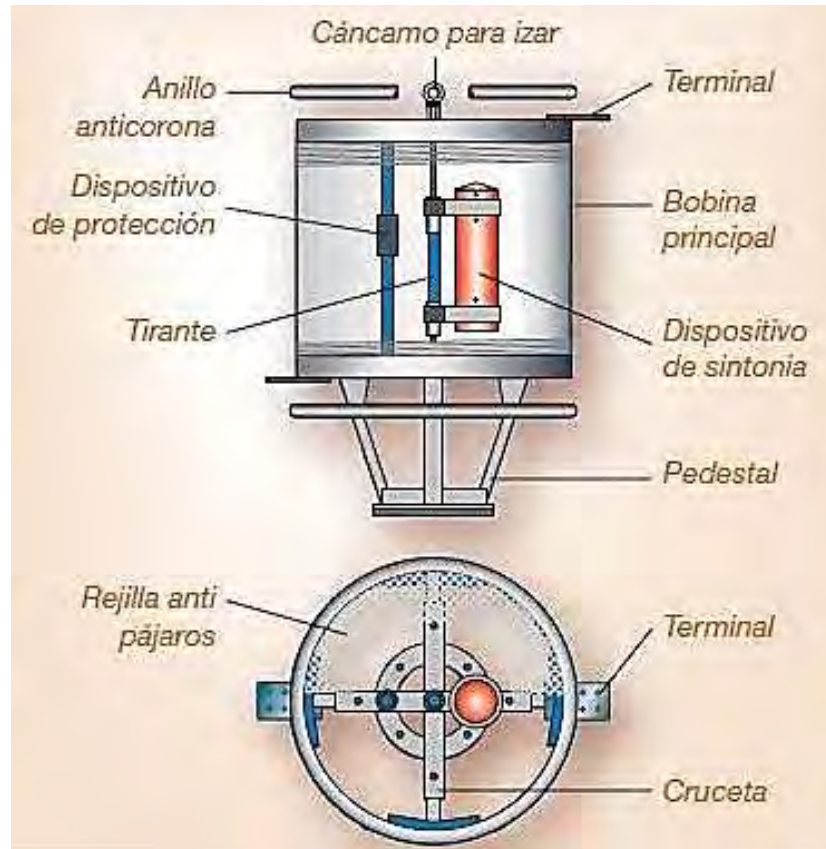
Principales componentes de una bobina de bloqueo
